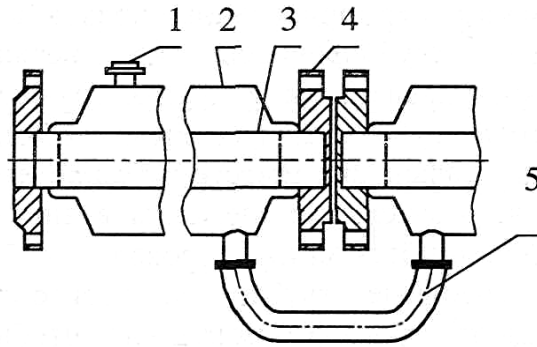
Схема участка трубопровода с рубашкой: 1 - штуцер; 2 - рубашка; 3 - обогреваемый трубопровод; 4 - фланец плоский приварной; 5 - обводная труба
